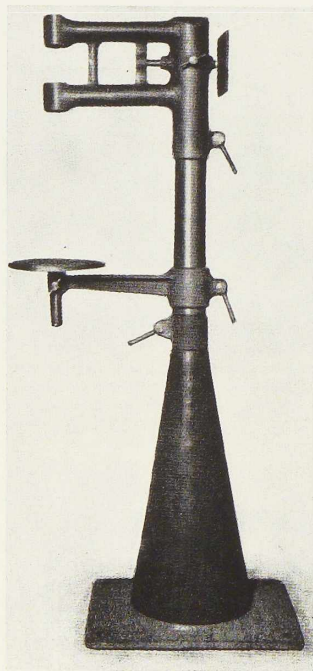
Bâti de foreuse en tôle et tubes soudés au chalumeau (d'après Schmelzschweissung).
